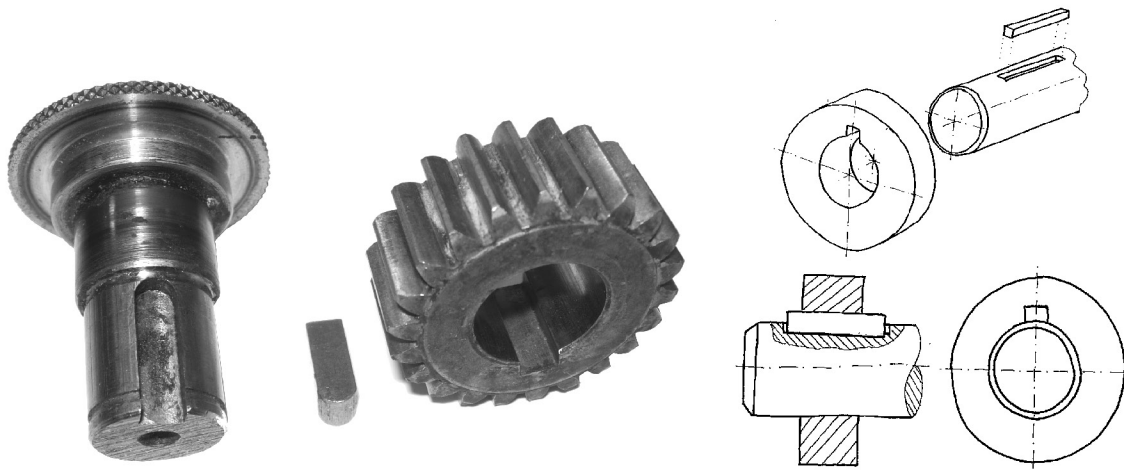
Subconjunto de eje, chaveta y rueda dentada desmontado (izquierda) y dibujo de eje, rueda y chaveta en explosión y montado (derecha)
